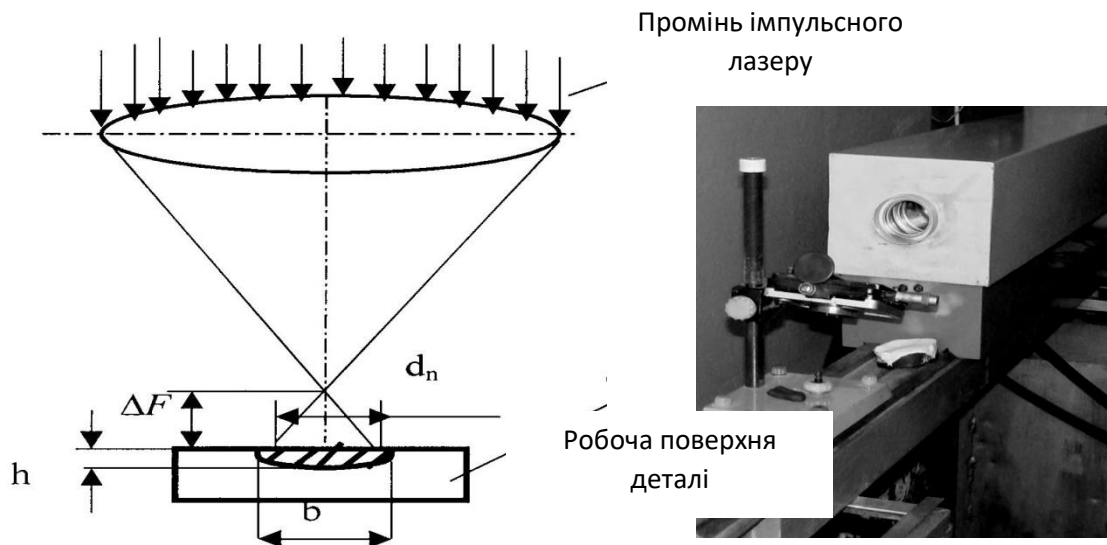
Сфокусована пляма на робочій поверхні деталі при обробці імпульсним лазером ГОС -1001
